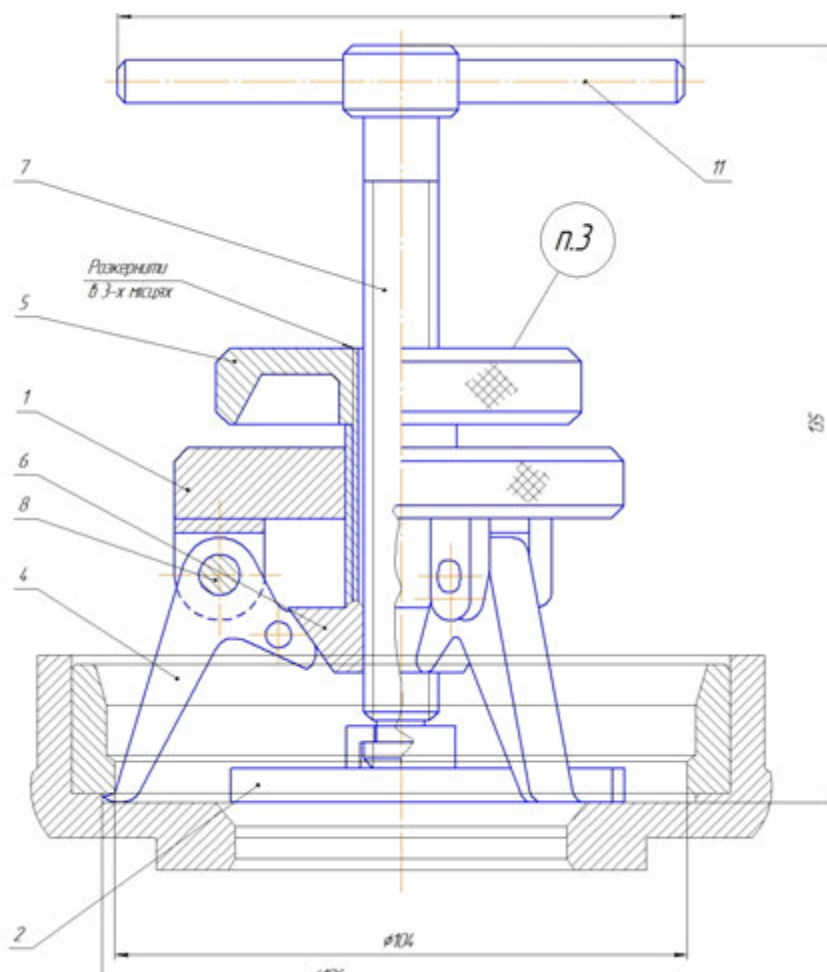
Знімач зовнішнього кільця підшипника 12213.
